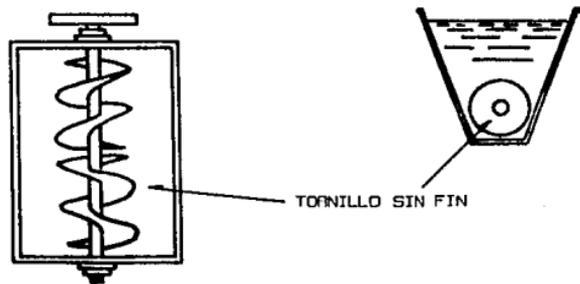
MEZCLADORAS CON TORNILLO SIN FIN.
